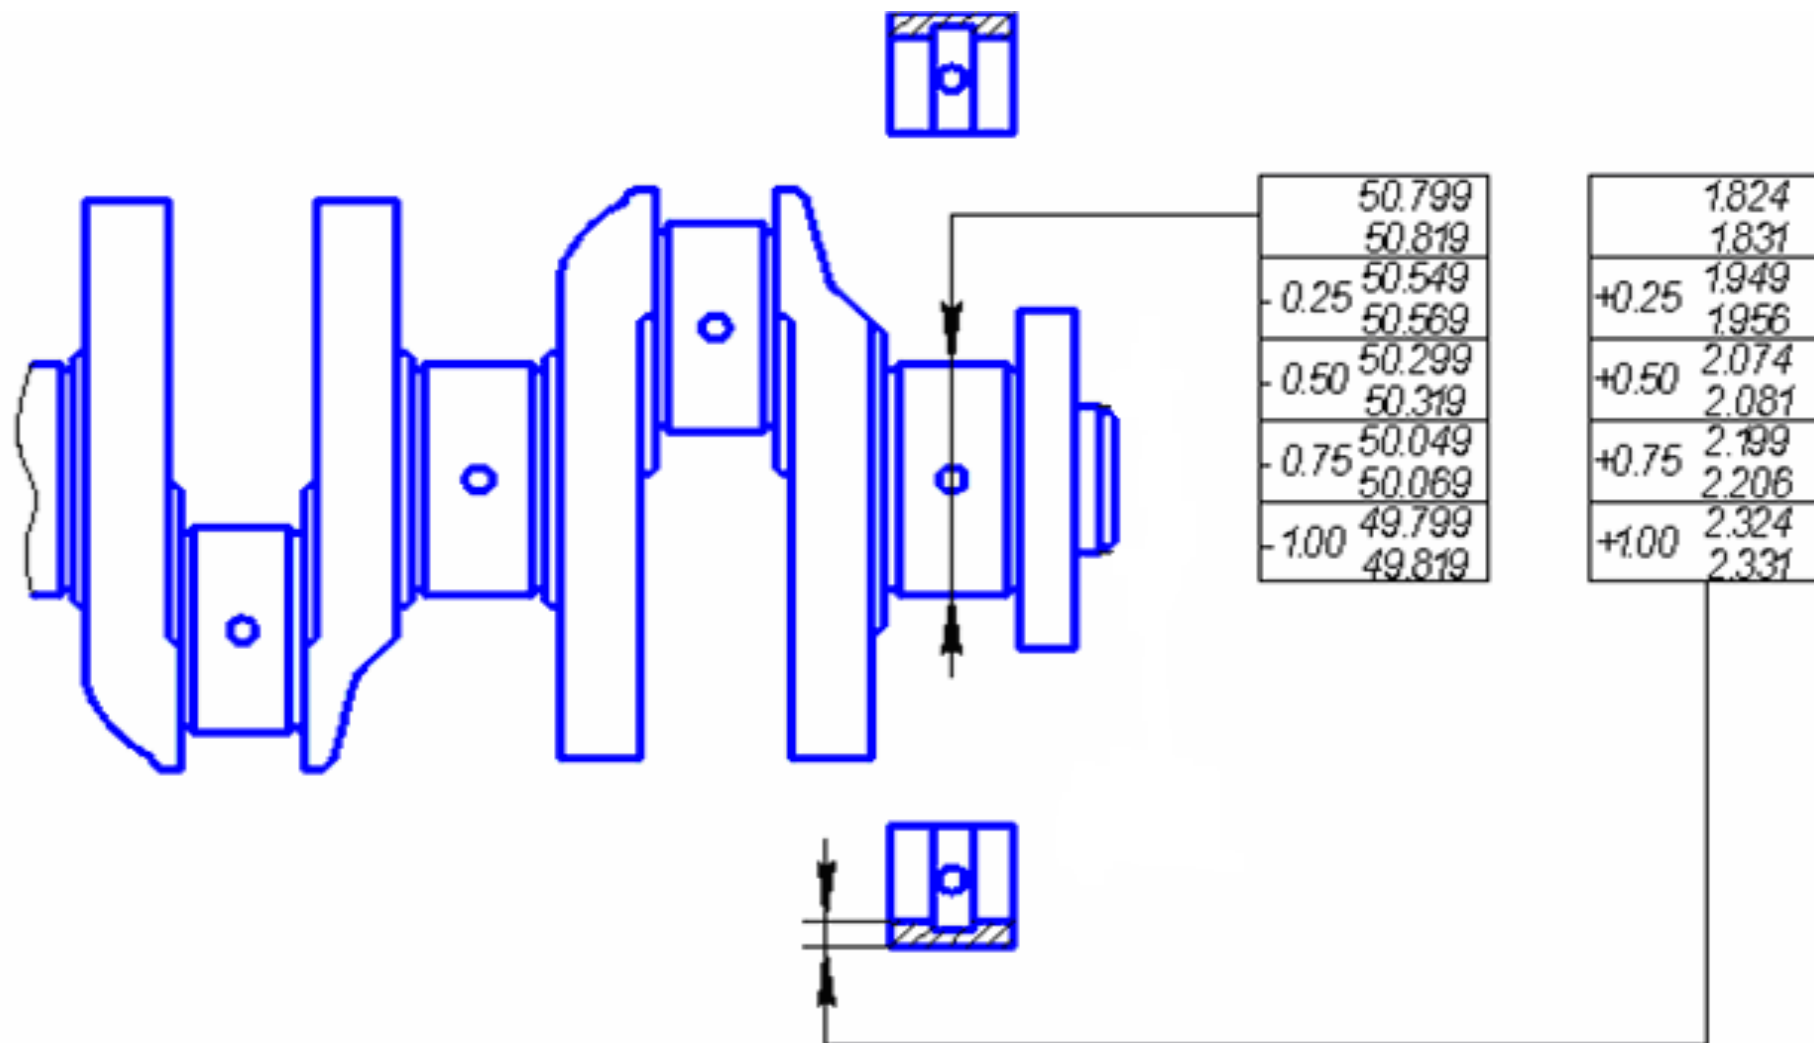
Основные размеры коленчатого вала автомобиля ВАЗ коренных шеек
